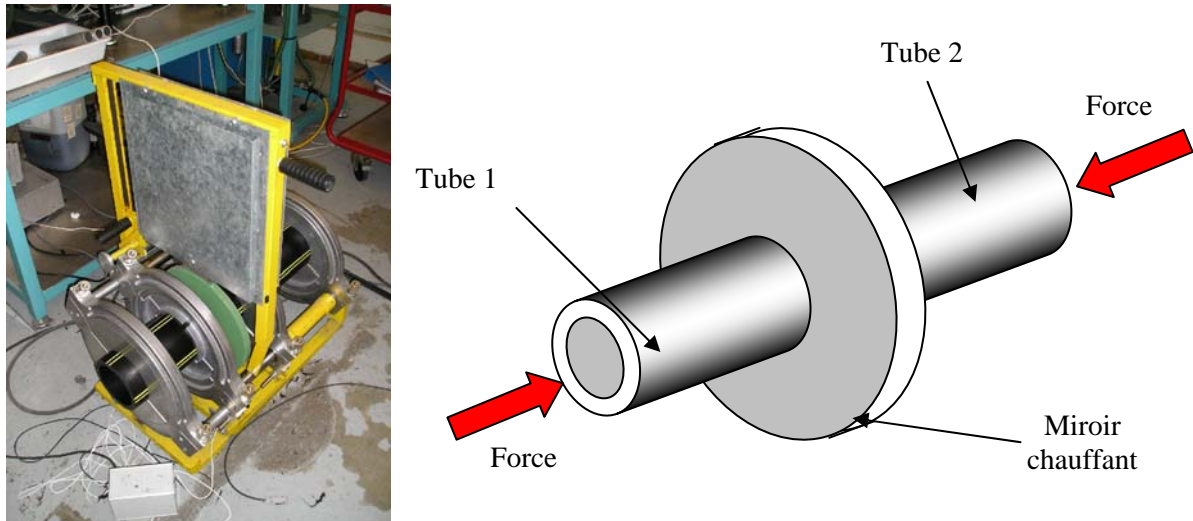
chauffage des tubes lors du soudage bout à bout
